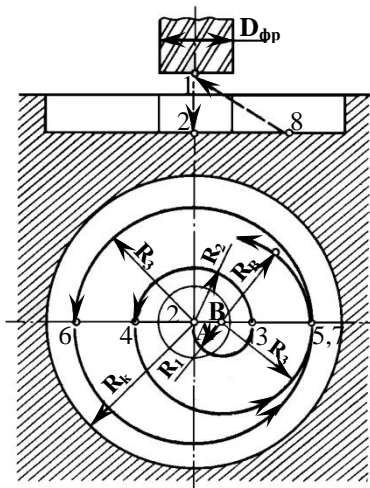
Схема фрезерування закритої площини, що обмежена колом, за траєкторією двополюсної спіралі
